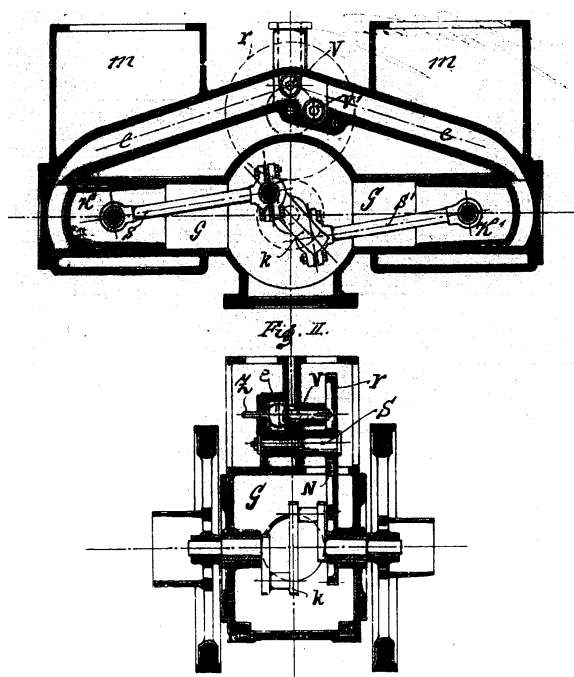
«Оппозитный» двигатель Б. Луцкого
